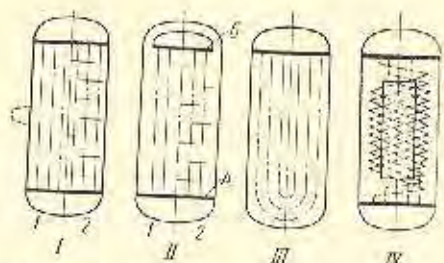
Основные конструктивные схемы цилиндрических кожухотрубных теплообменников с плоскими трубными решетками: I — прямоугольный змеевик конструкции и жесткой (с компенсатором в корпусе); 2 — с перегородками; II — с плавающей головкой; III — с U-образными трубами; IV — с пачками трубами и сердечником, жесткой соединенным с трубными решетками
